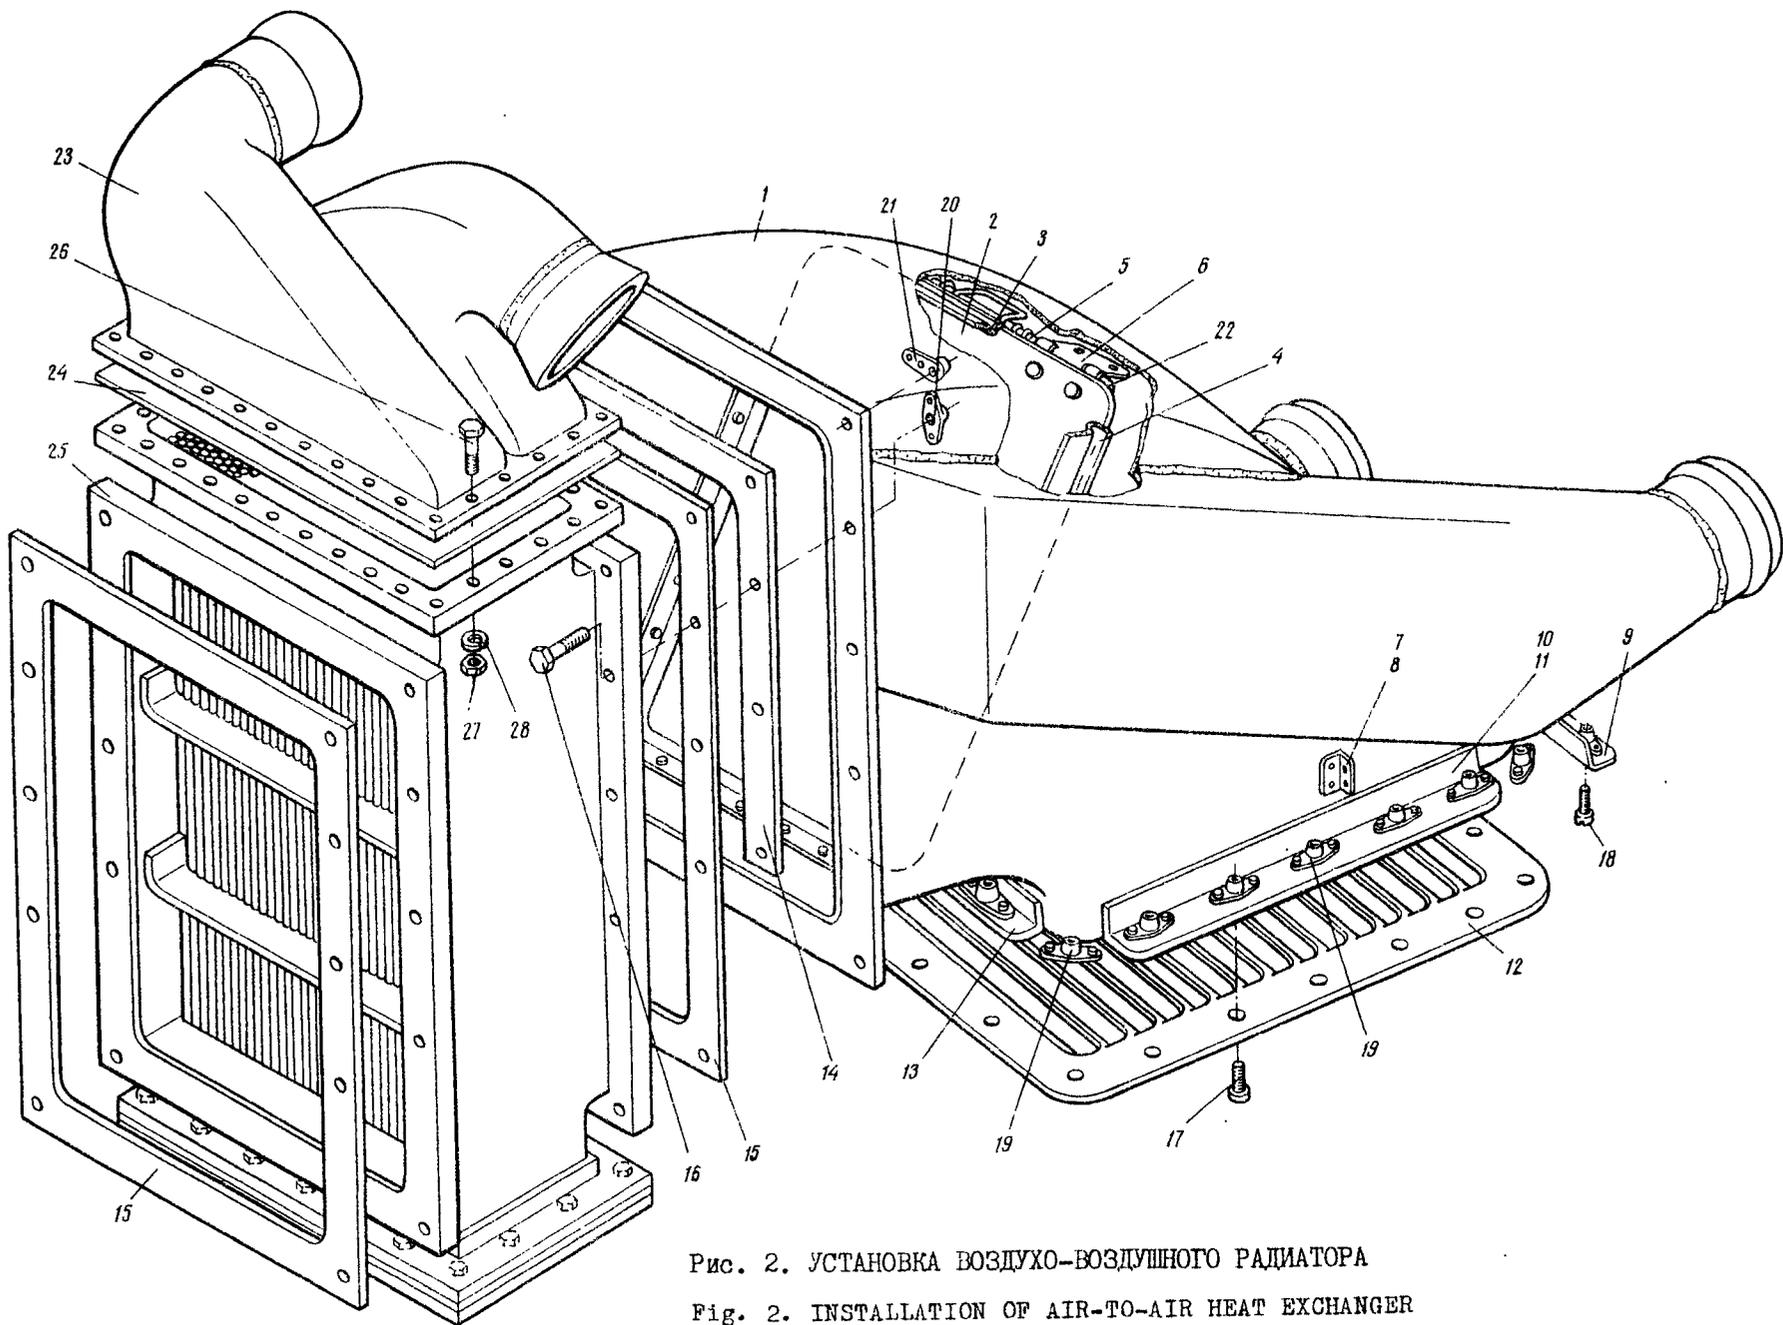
УСТАНОВКА ВОЗДУХО-ВОЗДУШНОГО РАДИАТОРА
